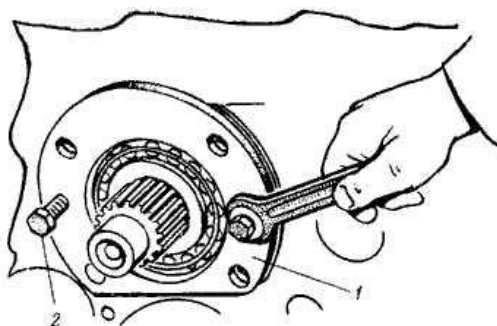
Выпрессовка стакана подшипника вторичного вала:
